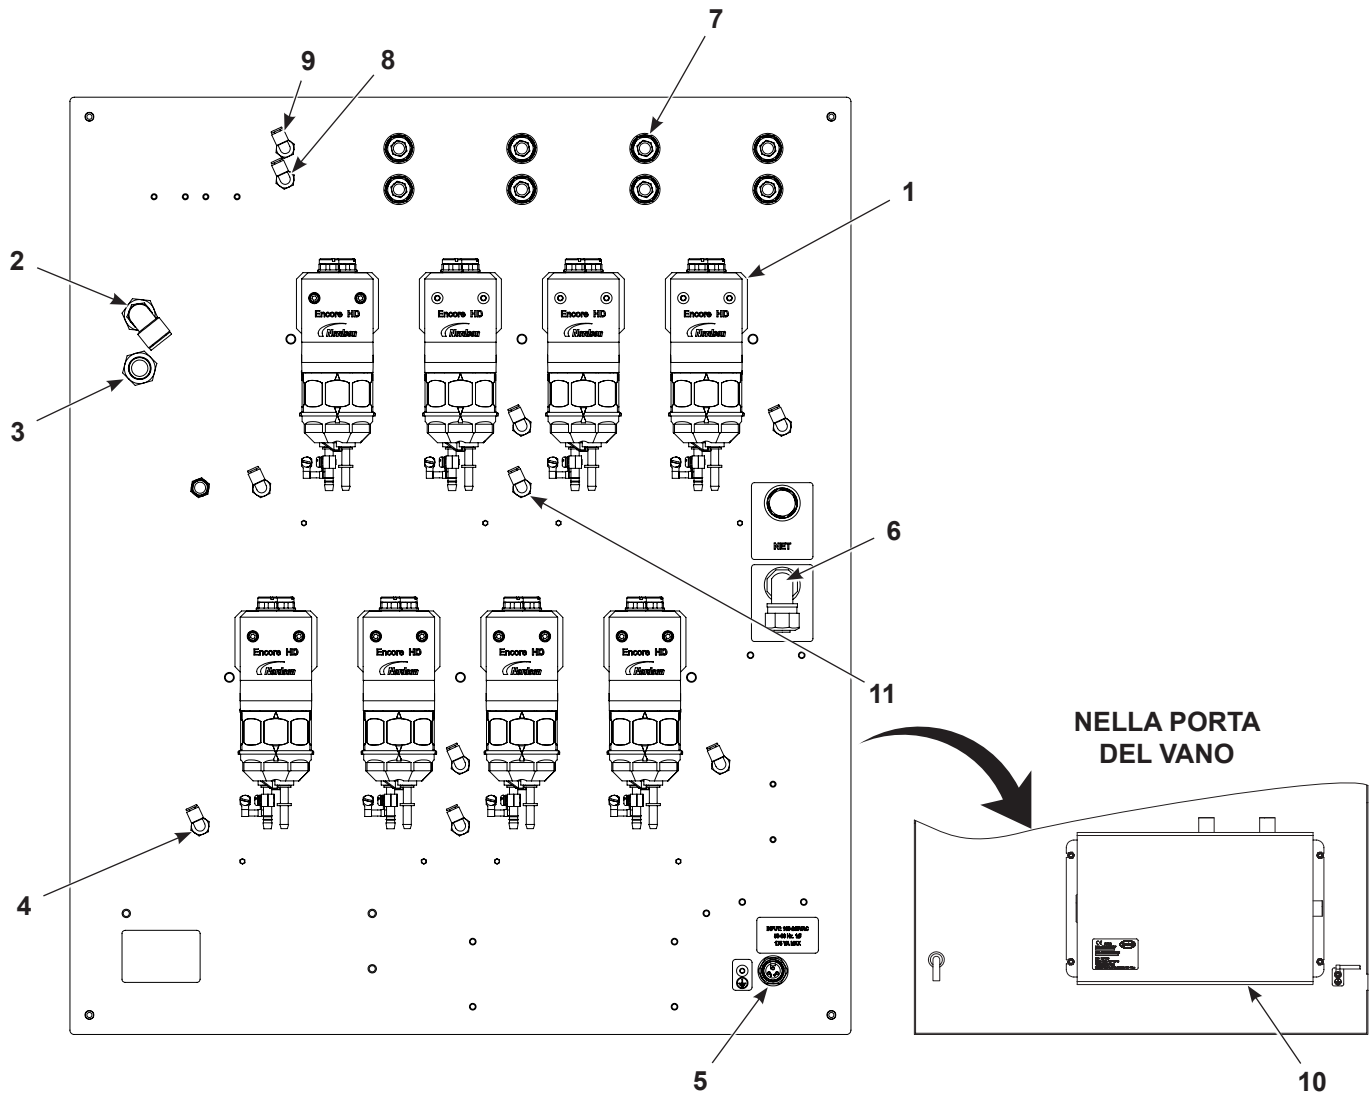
Componenti esterni del pannello pompe (nell'immagine il pannello ad otto pompe)
